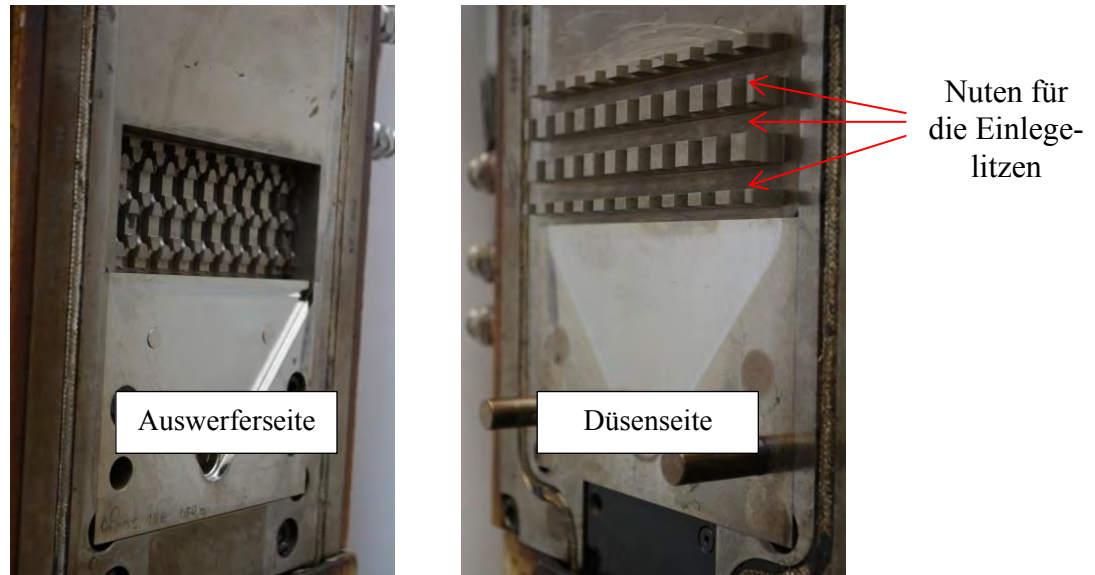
Gefertigte Werkzeugeinsätze mit Zahngeometrie für die Versuchsplatte
